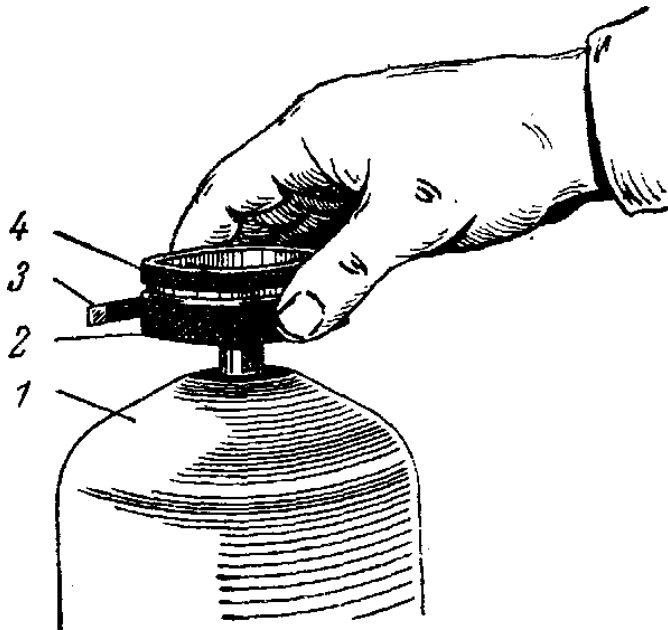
Перевірка стану відцентрового оливоочисника приладом КИ-1308В: 1 – ковпак центрифуги; 2 – корпус риладу; 3 – язичок; 4 – маховичок.
